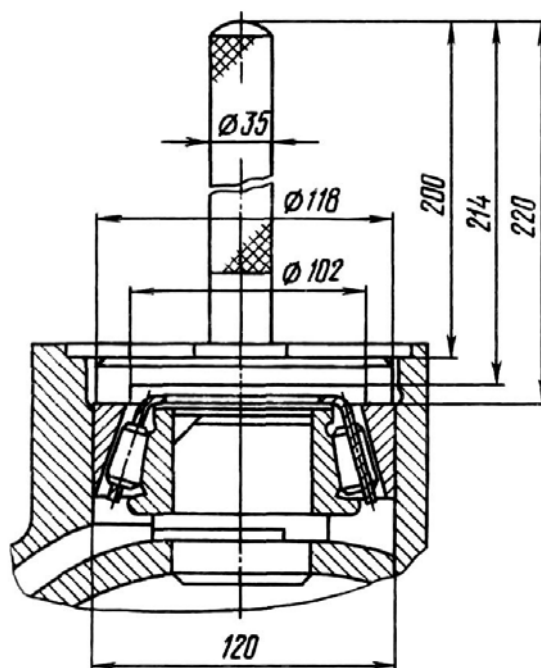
Запрессовка наружных колец подшипников в корпус поворотного кулака
